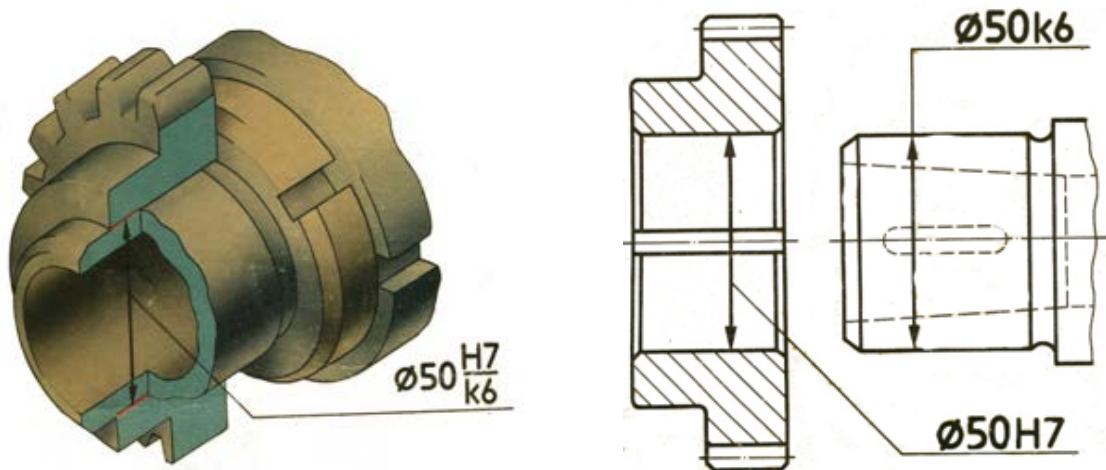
Шестерня на конце шпинделя токарного станка.
